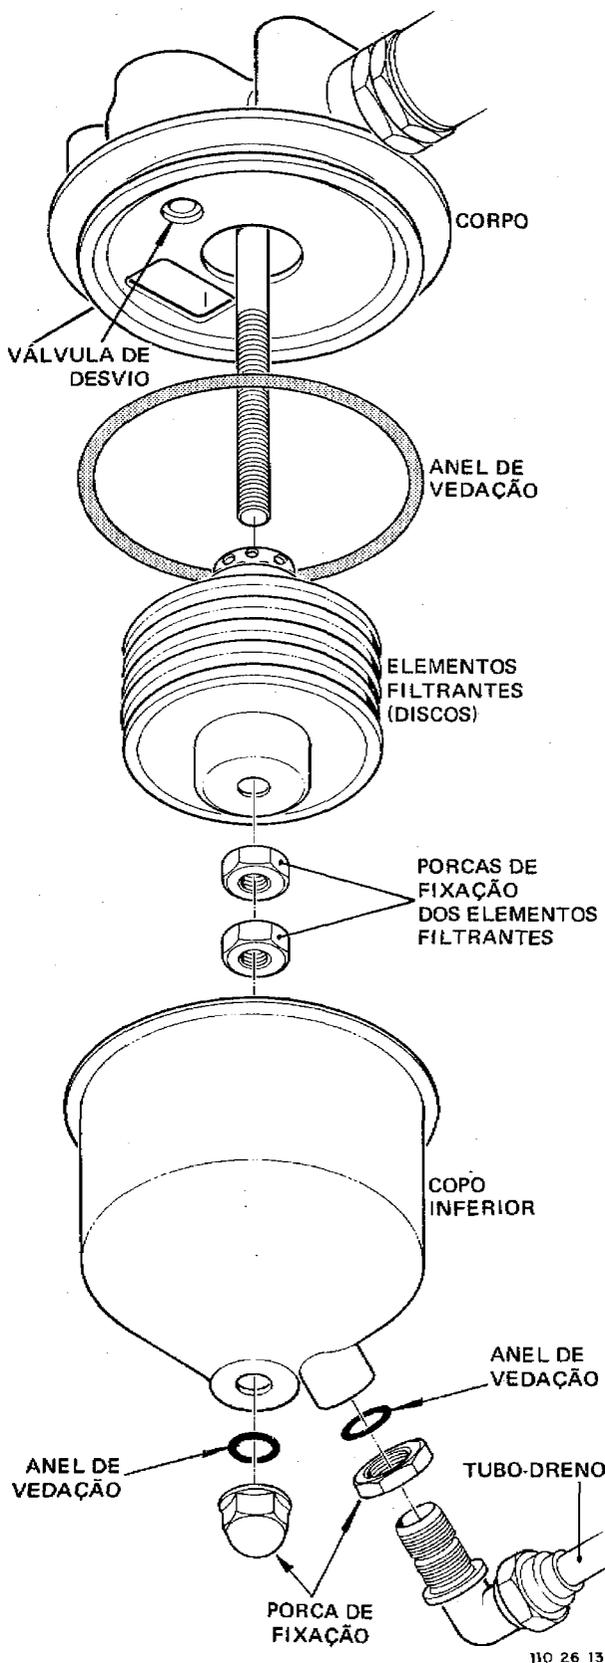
Instalação dos Elementos do Filtro de Combustível
